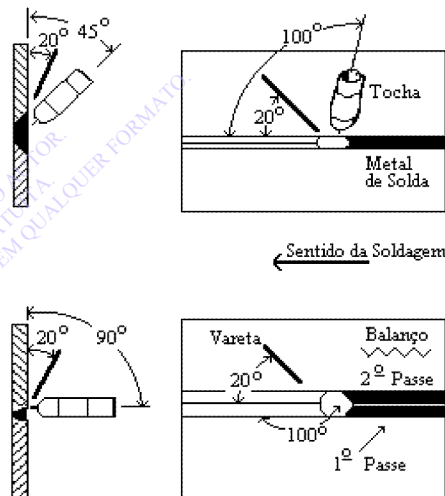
Soldagem TIG a Topo na Posição Horizontal: (a) 1º Passe; (b) 2º Passe.
